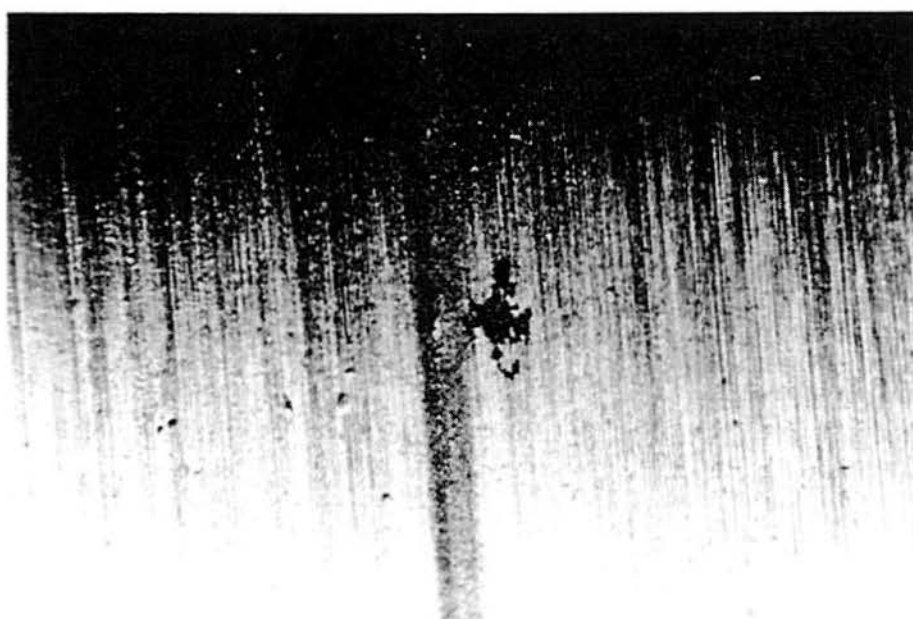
13B06A - Pista externa, LA, outro detalhe do dano na pista com arrancamento de material e alguns "pittings".
